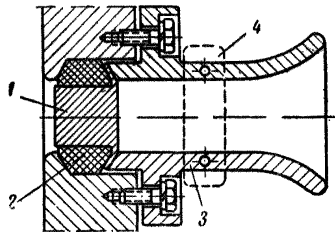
Кабельный ввод с металлической заглушкой.
